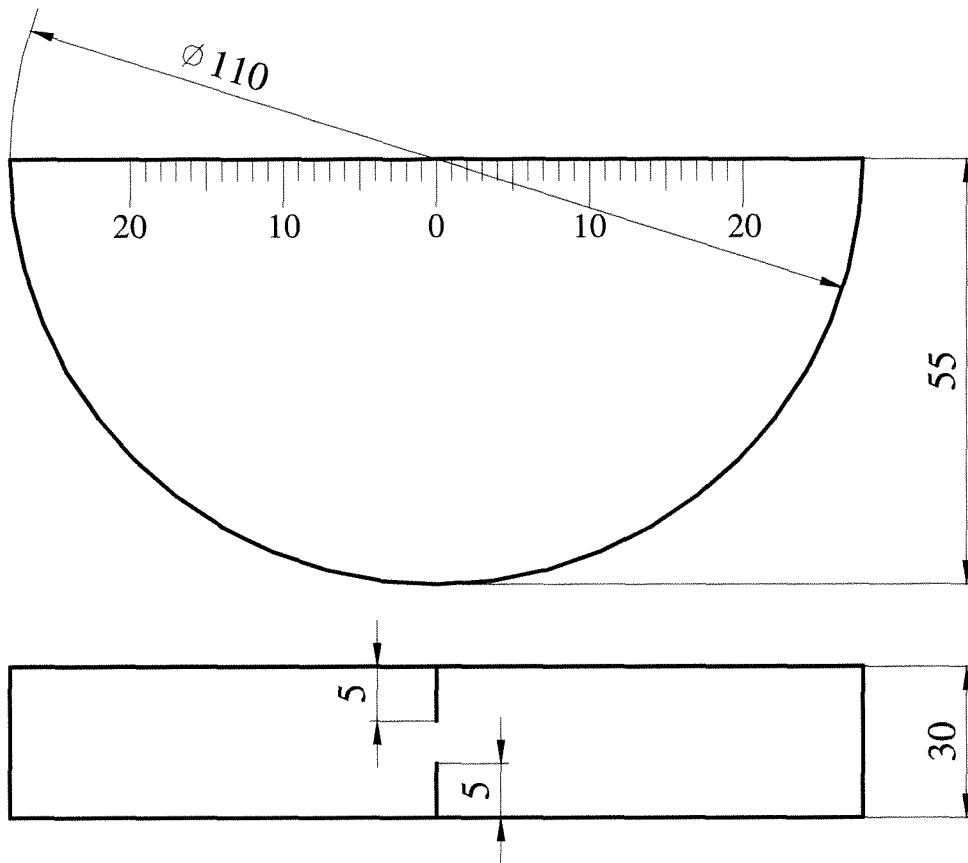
Стандартный образец СО-3 (материал - Ст.3)
